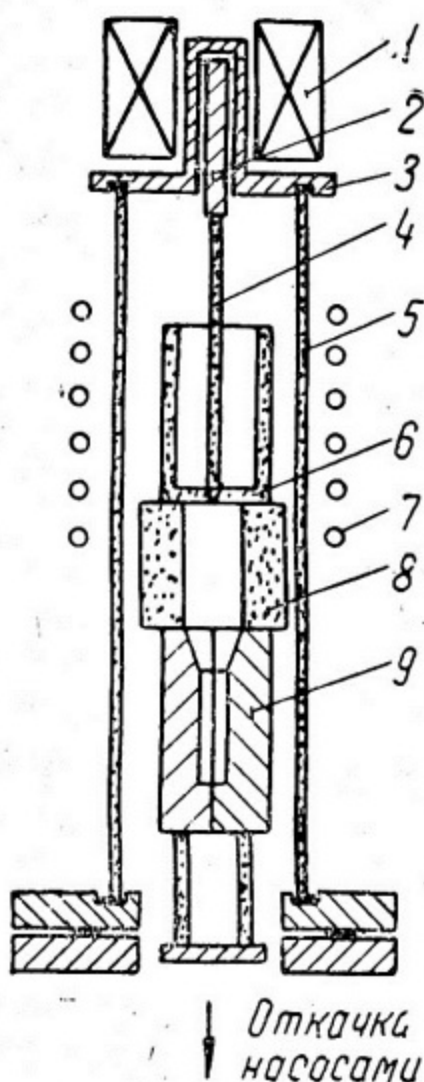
Схема установки для плавки в индукционной печи: 1 — электромагнит; 2 — стальная стержень; 3 — крышка (латунь); 4 — стержень, привертнутый к тиглю; 5 — кварцевая труба; 6 — тигель; 7 — индуктор; 8 — подставка; 9 — стальная разъемная изложница
